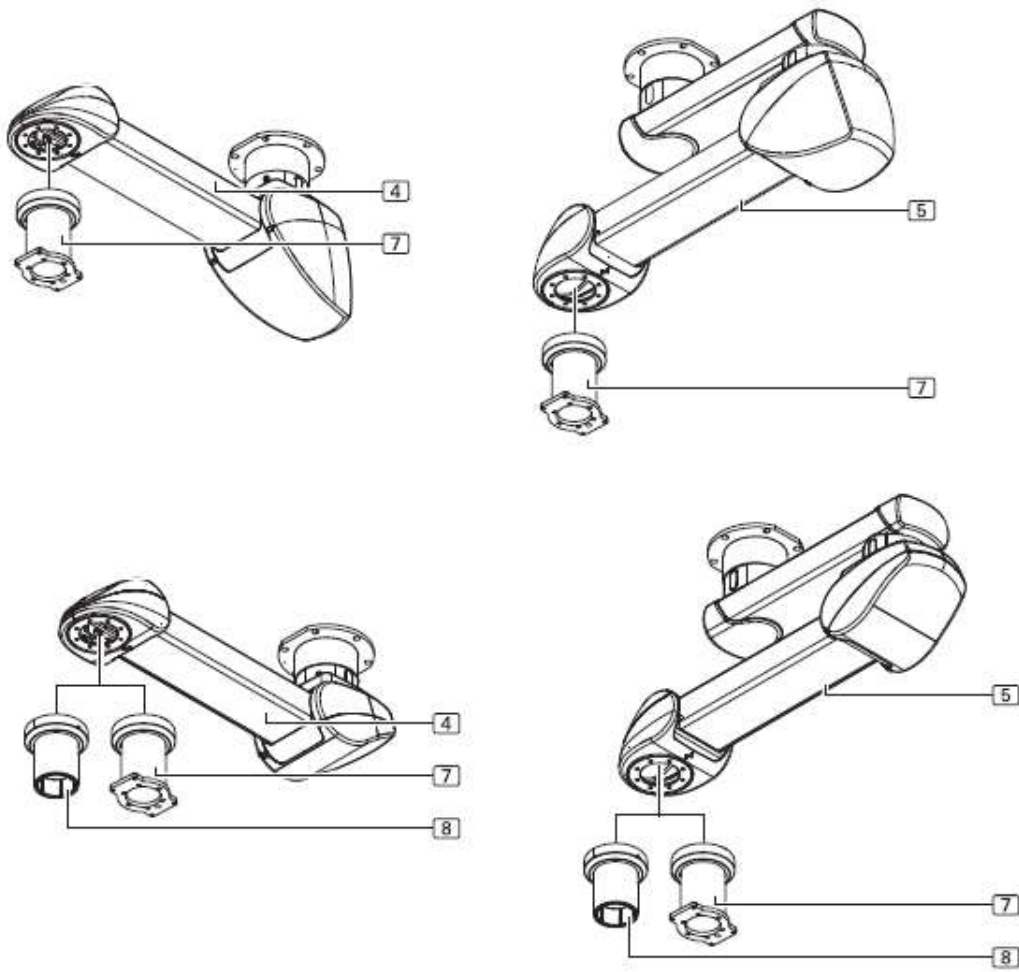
COLUMN SPRING, COLUMN SPRING XL
